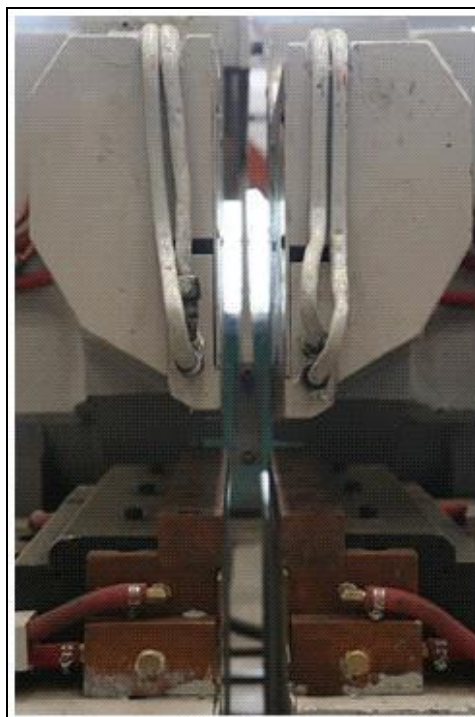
Pieza de la mordaza para soldadura
